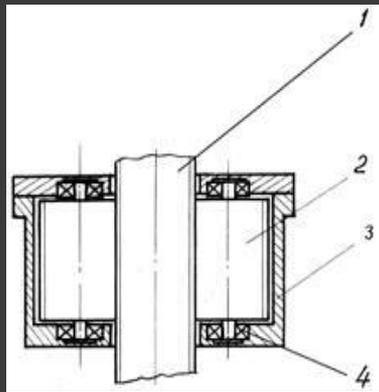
Передача винт – водило с резьбовыми роликами: 1 – винт; 2 – резьбовые ролики; 3 – водило; 4 – подшипники
